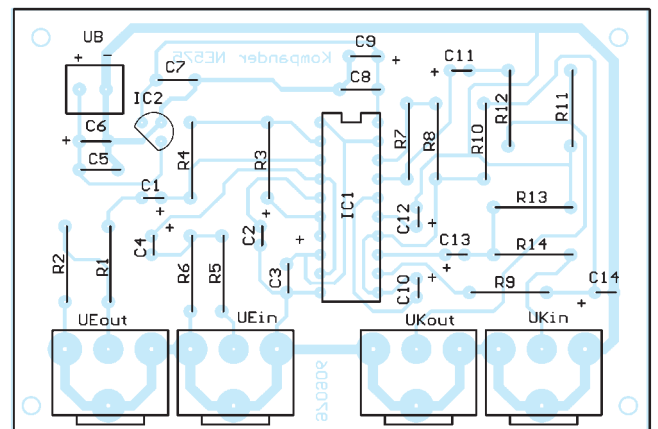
Auch die Kompanderplatine läßt sich in kürzester Zeit bestücken.
